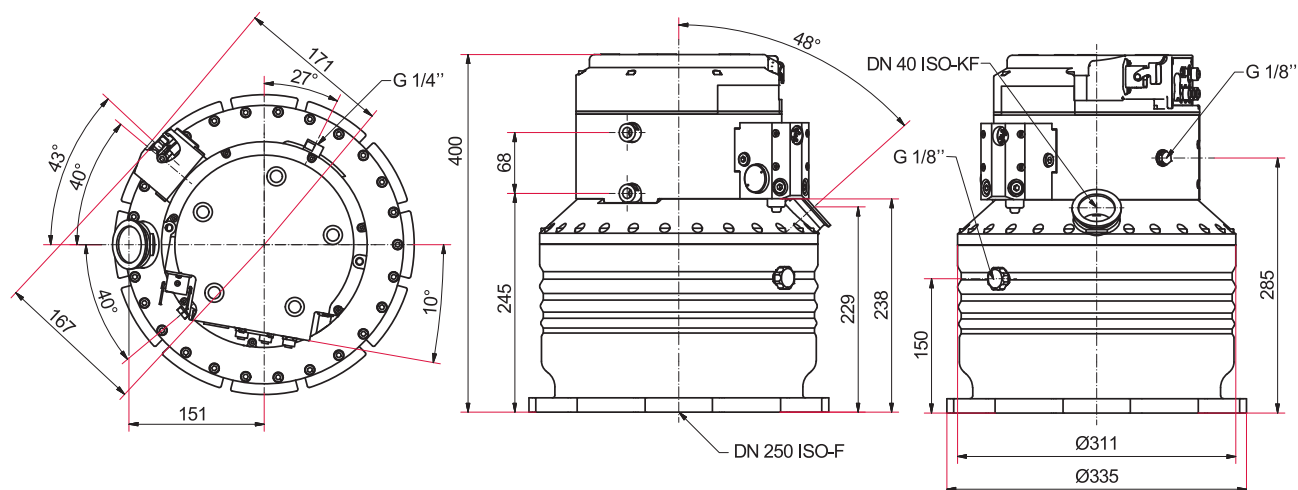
Dimensions HiPace 2300 U et HiPace 2300 UC | DN 250 ISO-F
